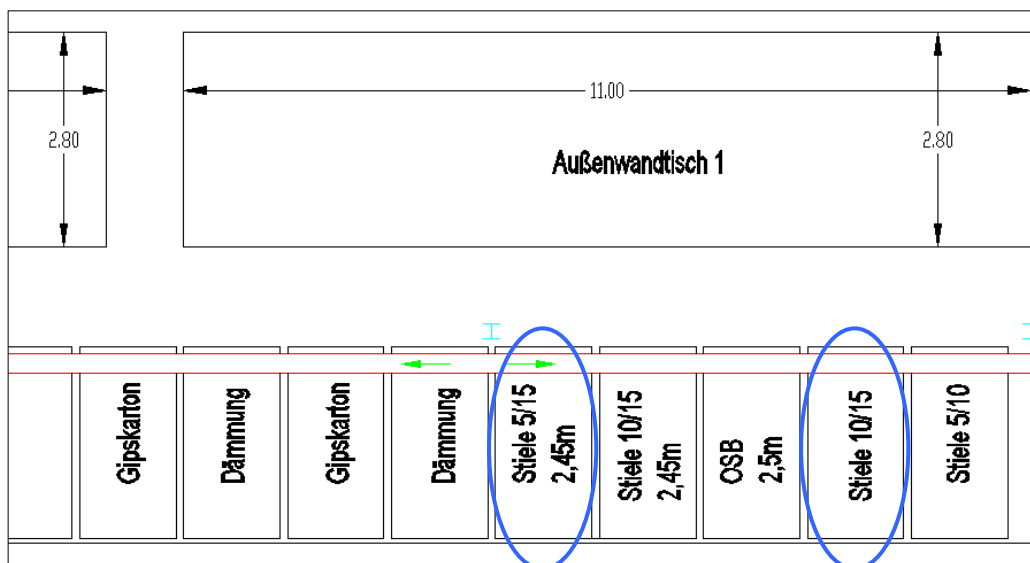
Ausschnitt des Werkslayout der Firma Gussek Haus
